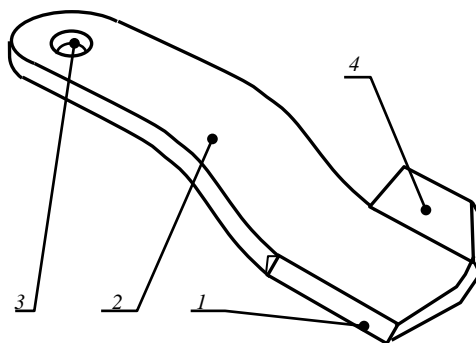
Типичная форма ножа косилки-измельчителя: 1 – режущая кромка; 2 – протяженная пластина; 3 – отверстие; 4 – подъемная пластинка
